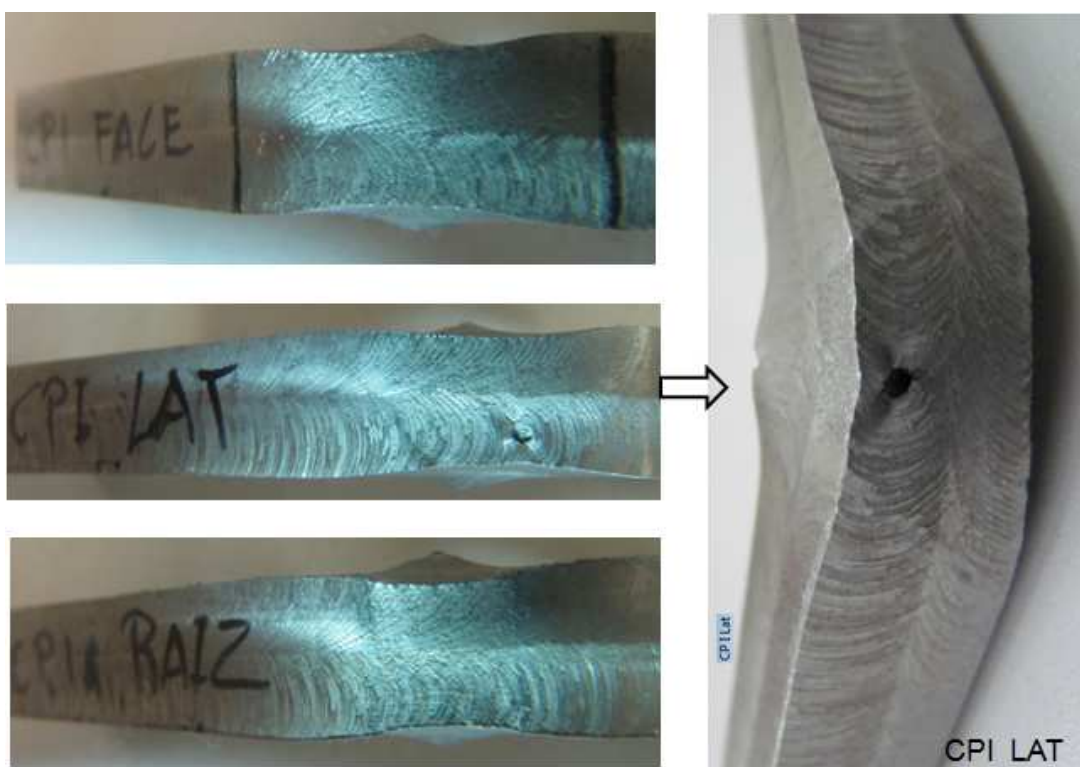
Resultado dos ensaios de dobra da condição de soldagem SS1 (CPI)
